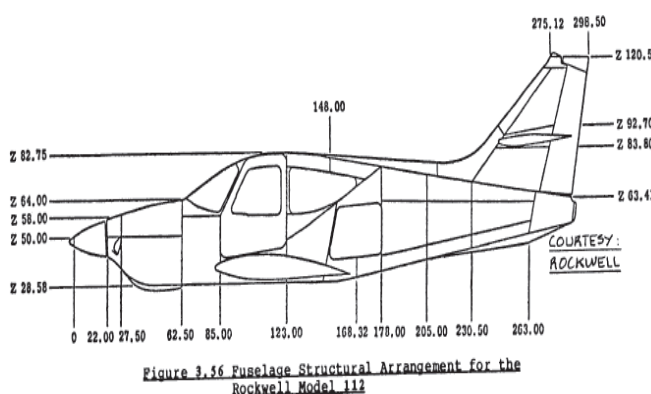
Plan de l'arrangement structurel d'un Rockwell 112
